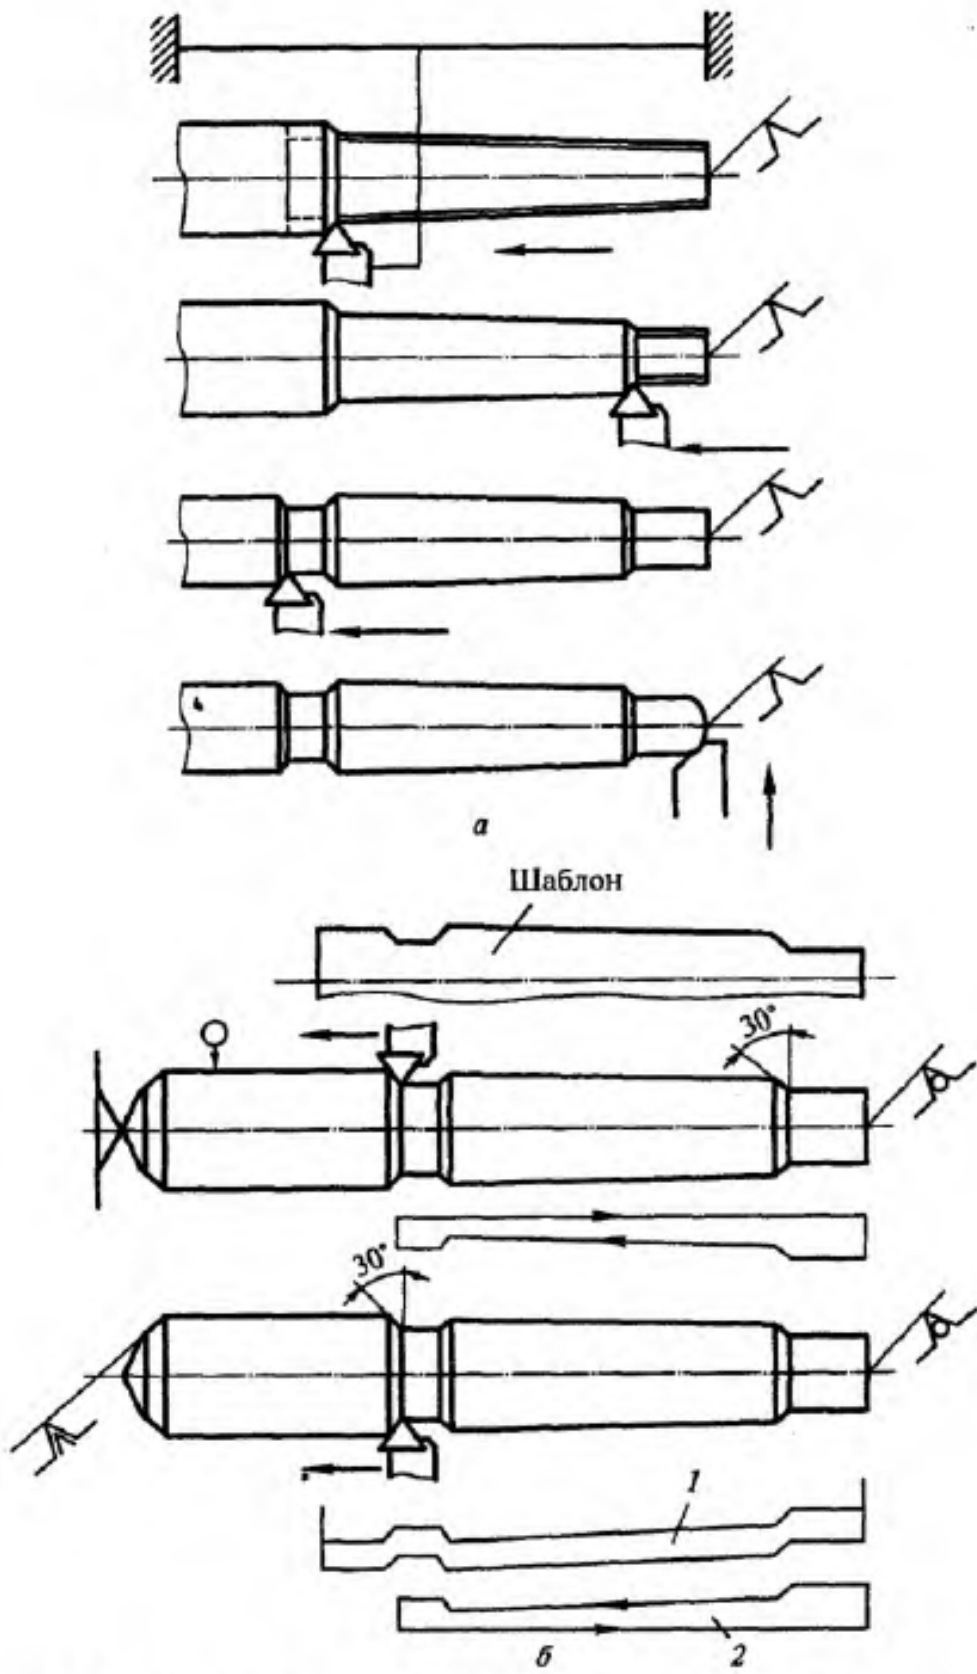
Схема токарного оброблення конічного хвостовика: а – на верстаті загального призначення; б – на гідрокопірувальному верстаті: 1 – чистовий шаблон; 2 – чорновий шаблон
